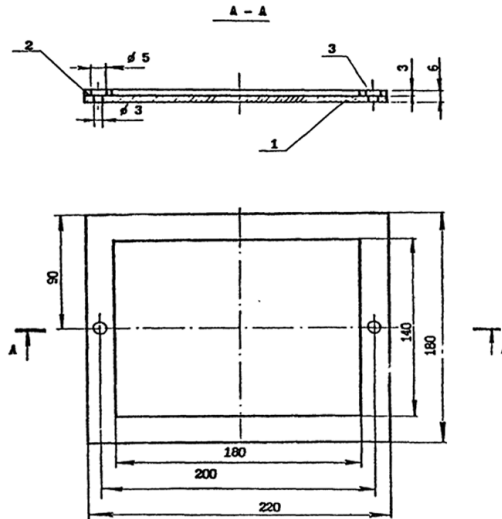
Форма для виготовлення зразків-пластин із робочого складу мастики.
